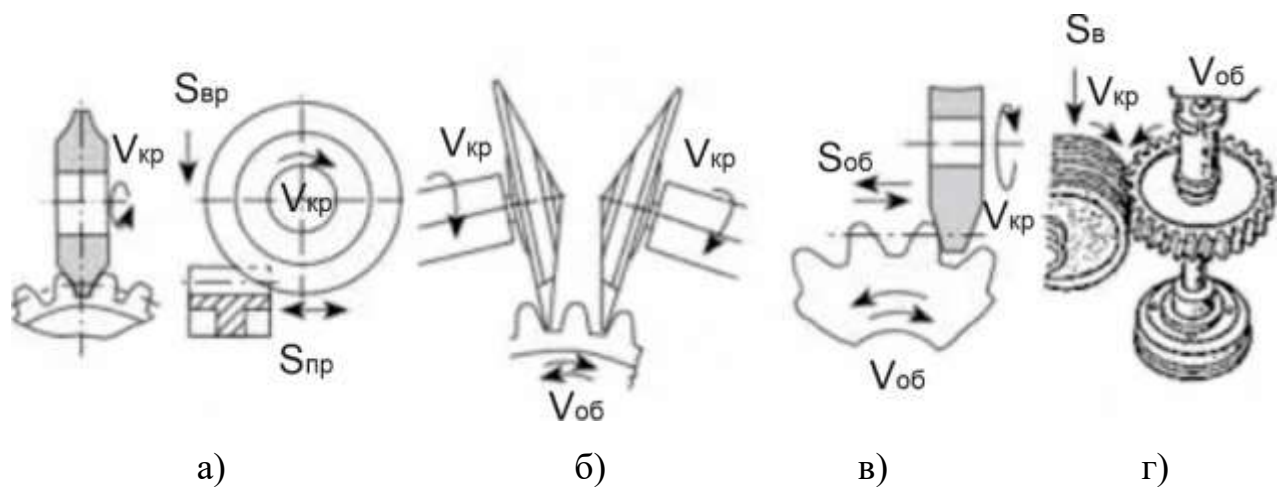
Схеми шліфування зубчастих коліс: а – шляхом копіювання; б - двома шліфувальними колами; в – одним шліфувальним колом; г - черв'ячним шліфувальним колом.
